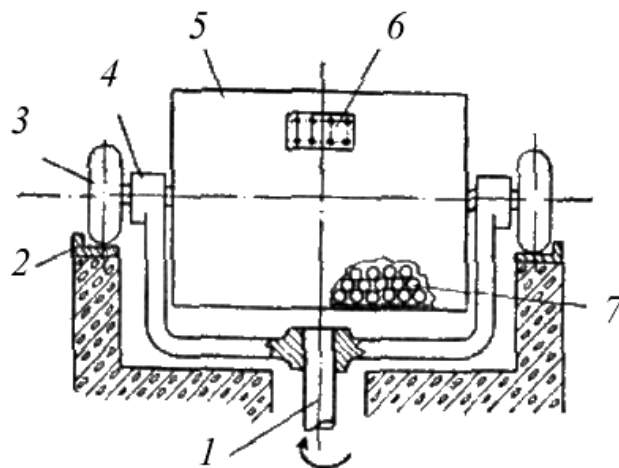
Гіроскопічний млин: 1 – приводний вал; 2 – опорна шайба;
